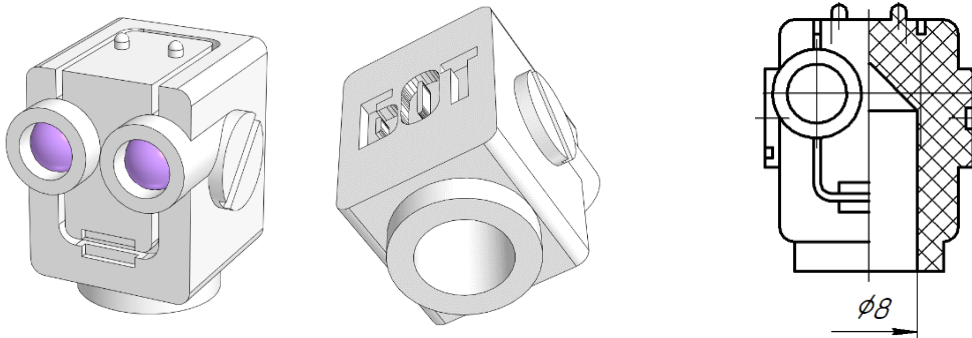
Образец изделия «Колпачок» и его профильный вид с местным разрезом.
